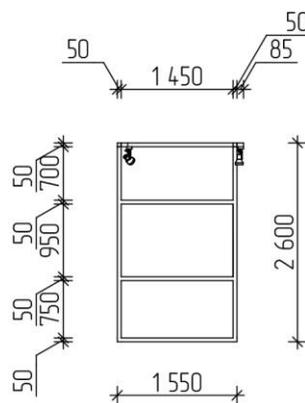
Чертеж стенда. Вид сбоку
